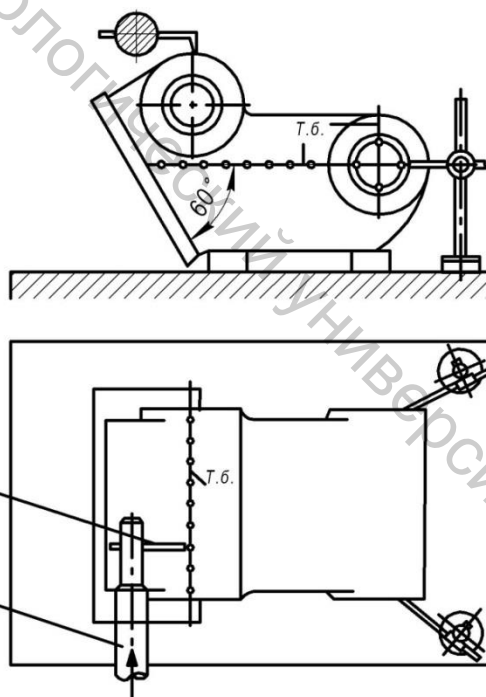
Реальное базирование заготовки на столе станка
